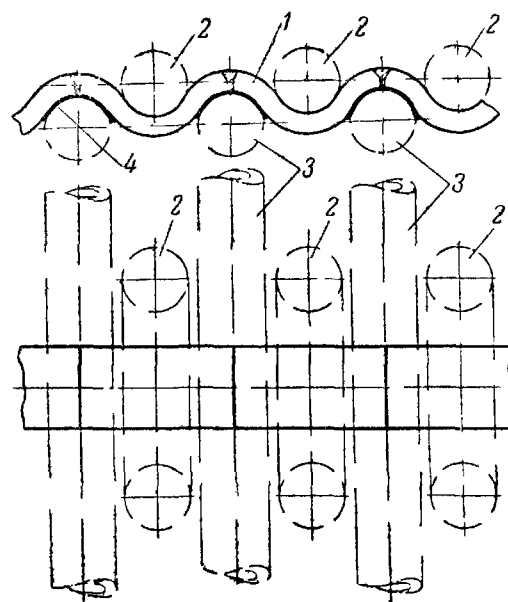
Крепление пароперегревателя котла ТП-170 I.
